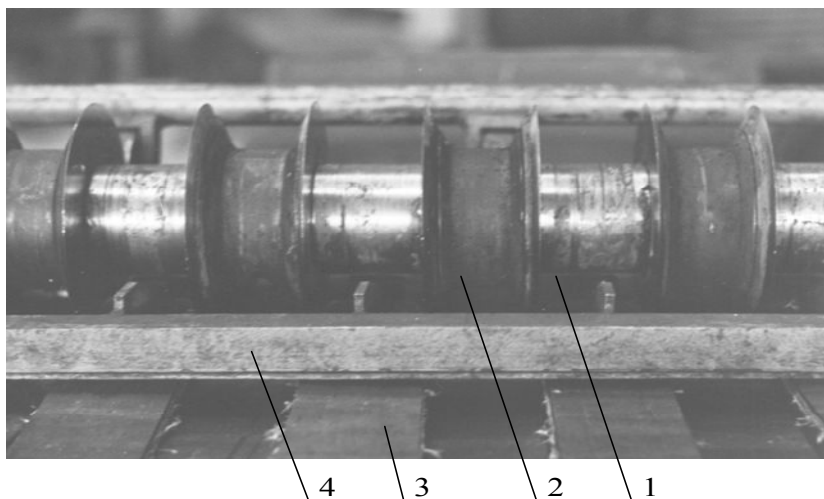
Ножовий блок верстата для різання конвеєрної стрічки
